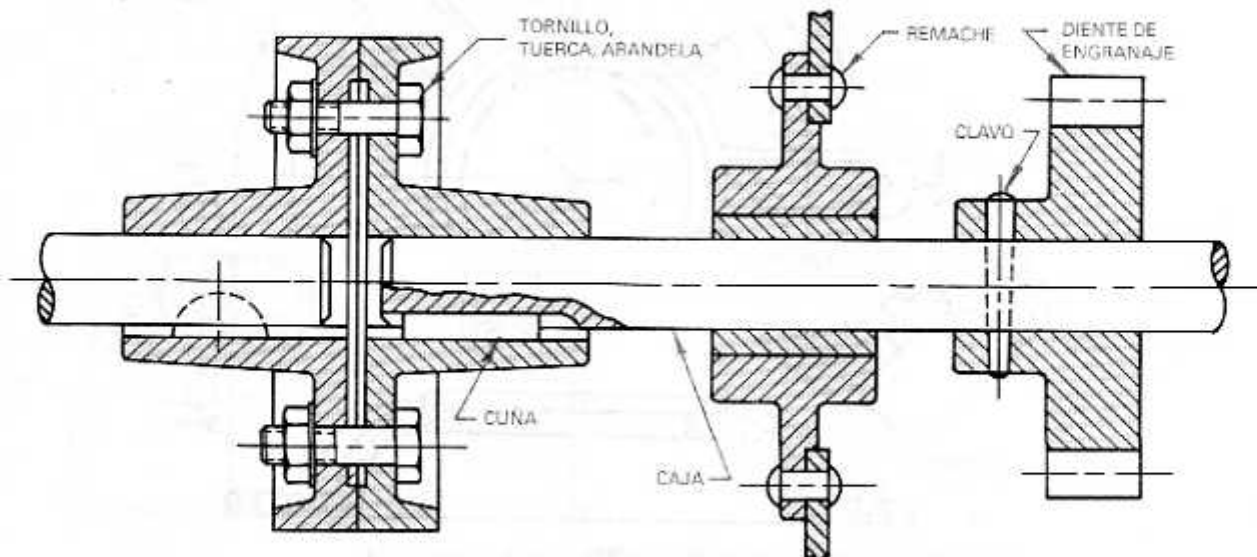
Secciones no aseguradas a pesar de que el plano de corte los atraviesa.
